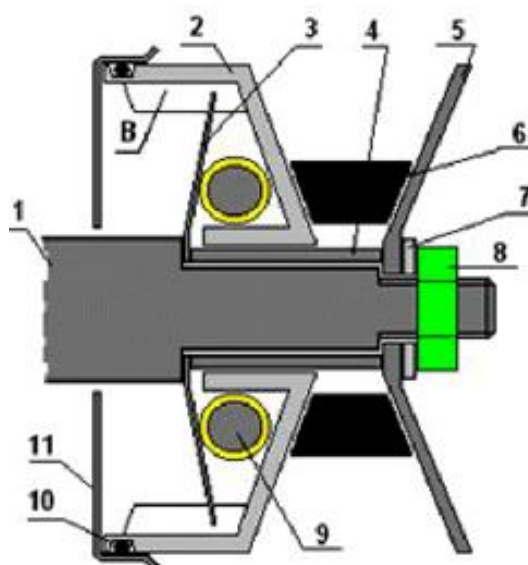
Центробежный механизм натяжения ремня: 1 – ведущий вал; 2 – подвижная половина шкива; 2 – упорная пластина; 4 – втулка; 5 – неподвижная половина шкива; 6 – вариаторный ремень; 7 – шайба; 8 – гайка; 9 – центробежные ролики; 11 - крышка
